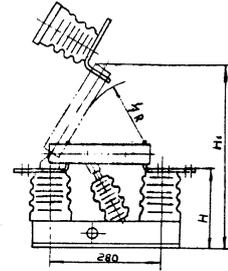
Разъединитель однополюсный типоразмера РЛВОМ 10-11/1000 II УХЛ2, Т2
